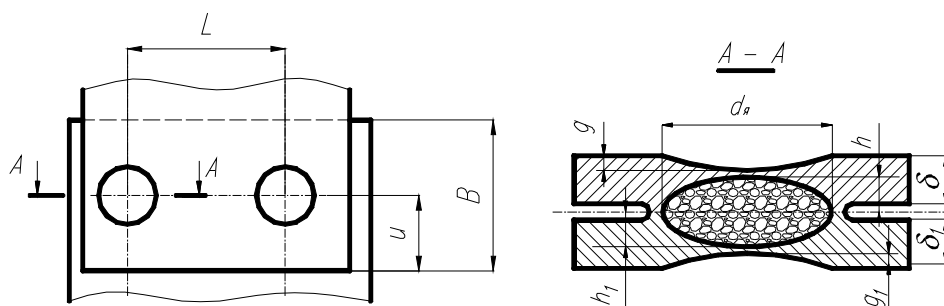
Параметри зварного з'єднання при контактному точковому зварюванні
